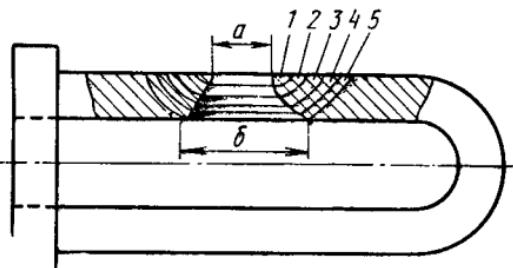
Схема вырезки канавки в дефектных сварных соединениях
